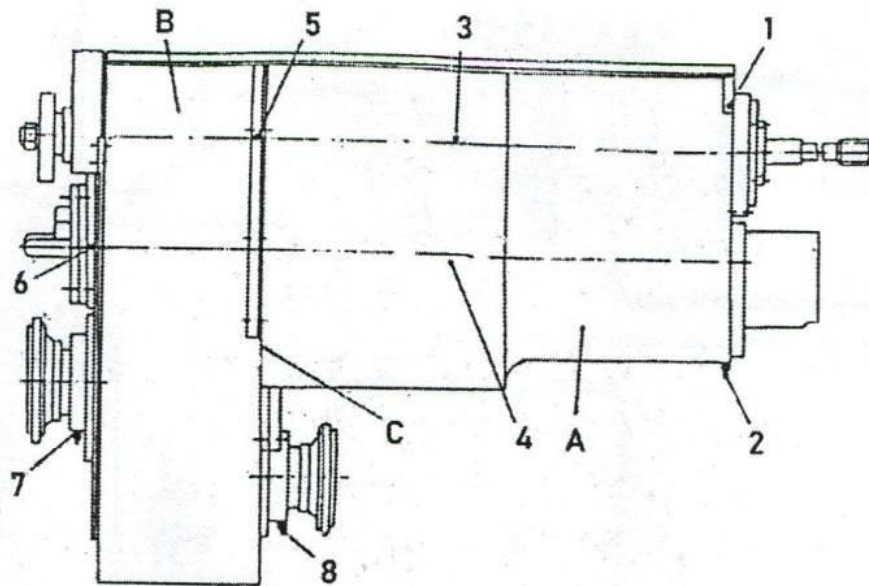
Коробка передач з роздавальною коробкою: 1-8 – точки контролю вібрації; А – коробка передач; В – роздавальна коробка; С – плоскість з'єднання коробки передач і роздавальної коробки
